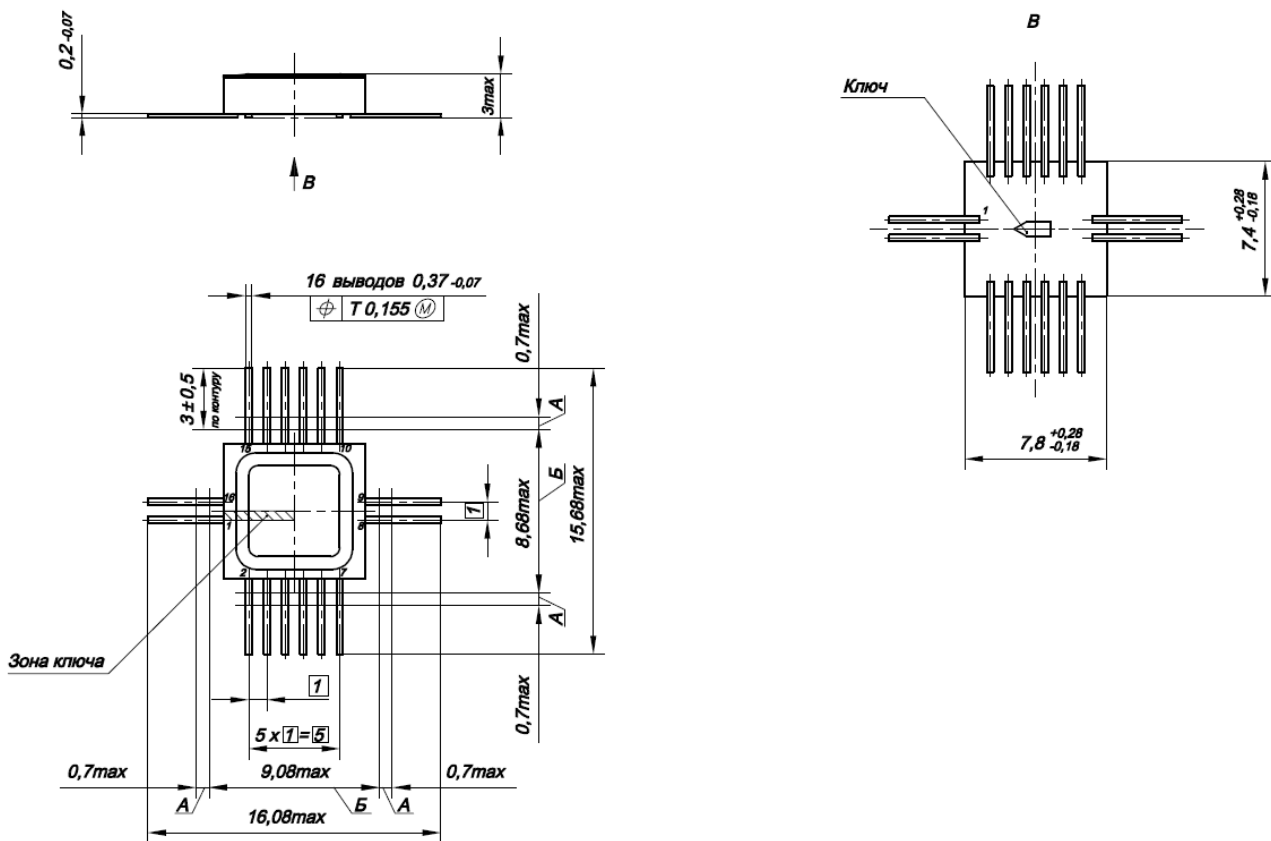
Габаритный чертеж корпуса Н04.16-1В, исполнение для микросхем 5559ИН13У1, У2, У3
